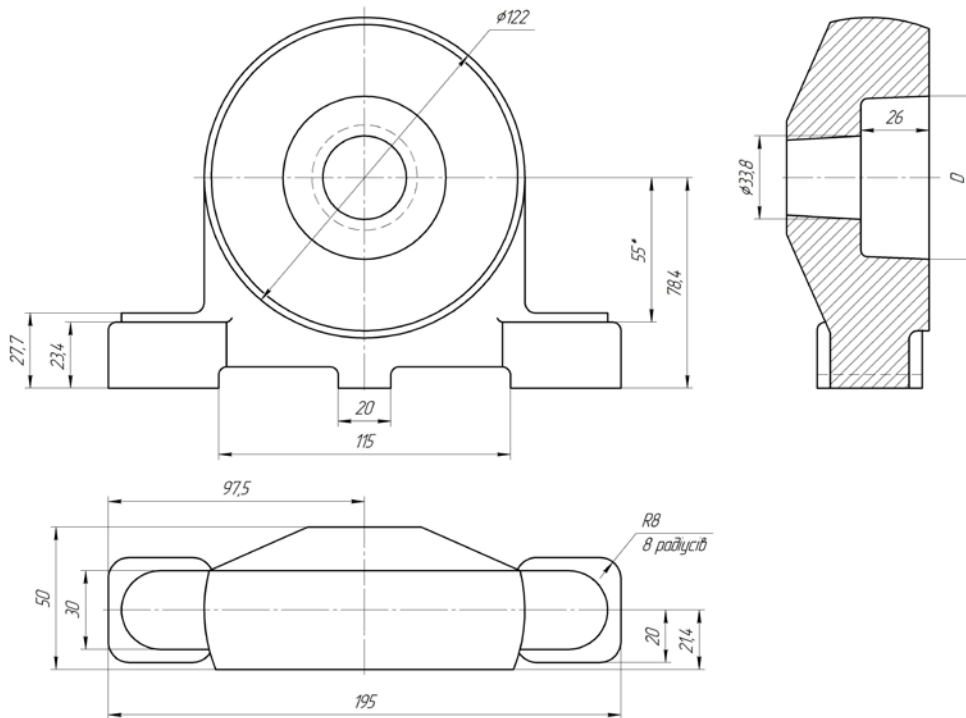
Ескіз заготовки деталі «Корпус підшипника»: * — розмір для довідок
